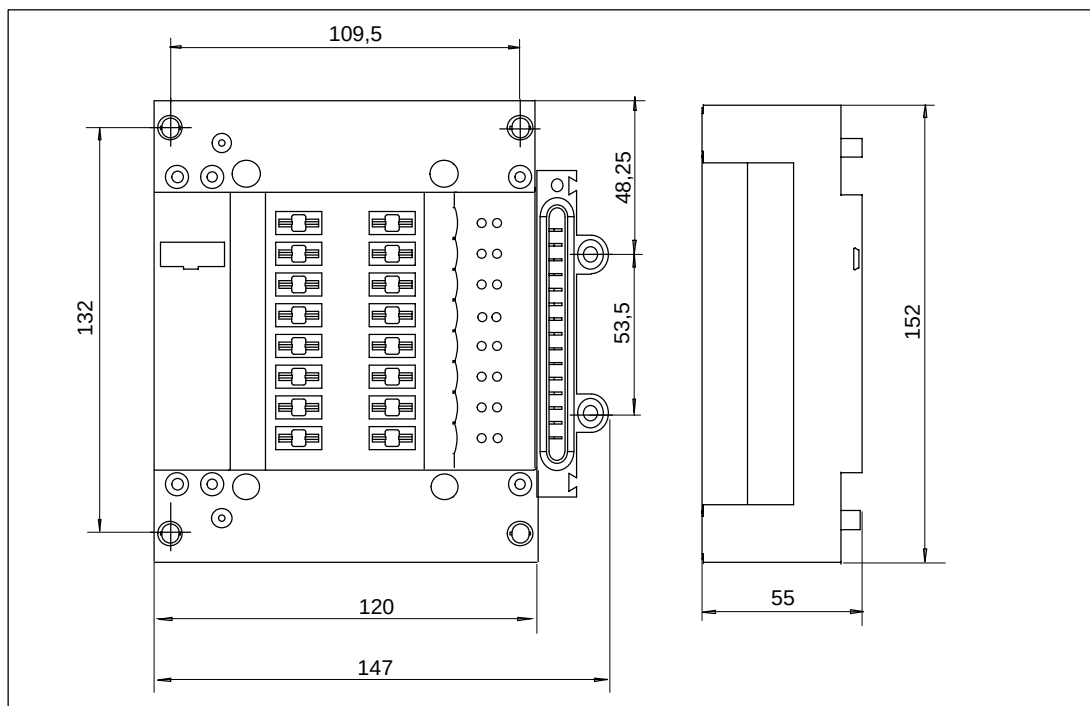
Disegno quotato Modulo Pneumatic Interface
